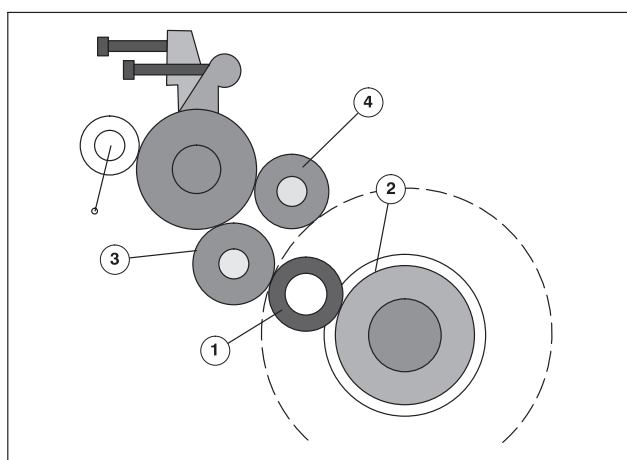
Регулировка накатных валиков с помощью установочного кольца
